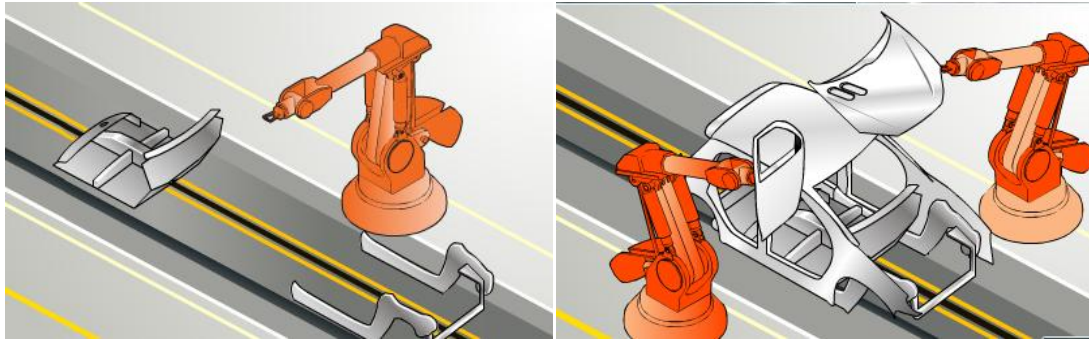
Línea principal de ensamblado. Fuente: Grupo PSA
